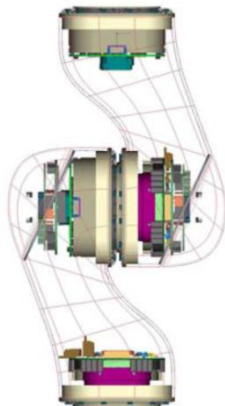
Vista frontale di un assemblaggio di 2 moduli. All'interno di può notare la componentistica meccanica ed elettronica
